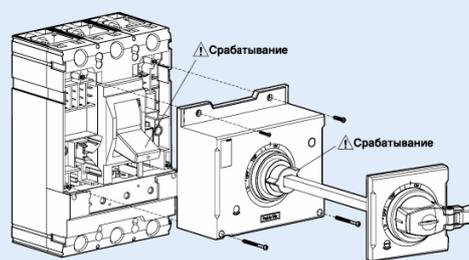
Габаритные и установочные размеры, способ установки выносных поворотных рукояток TS800
